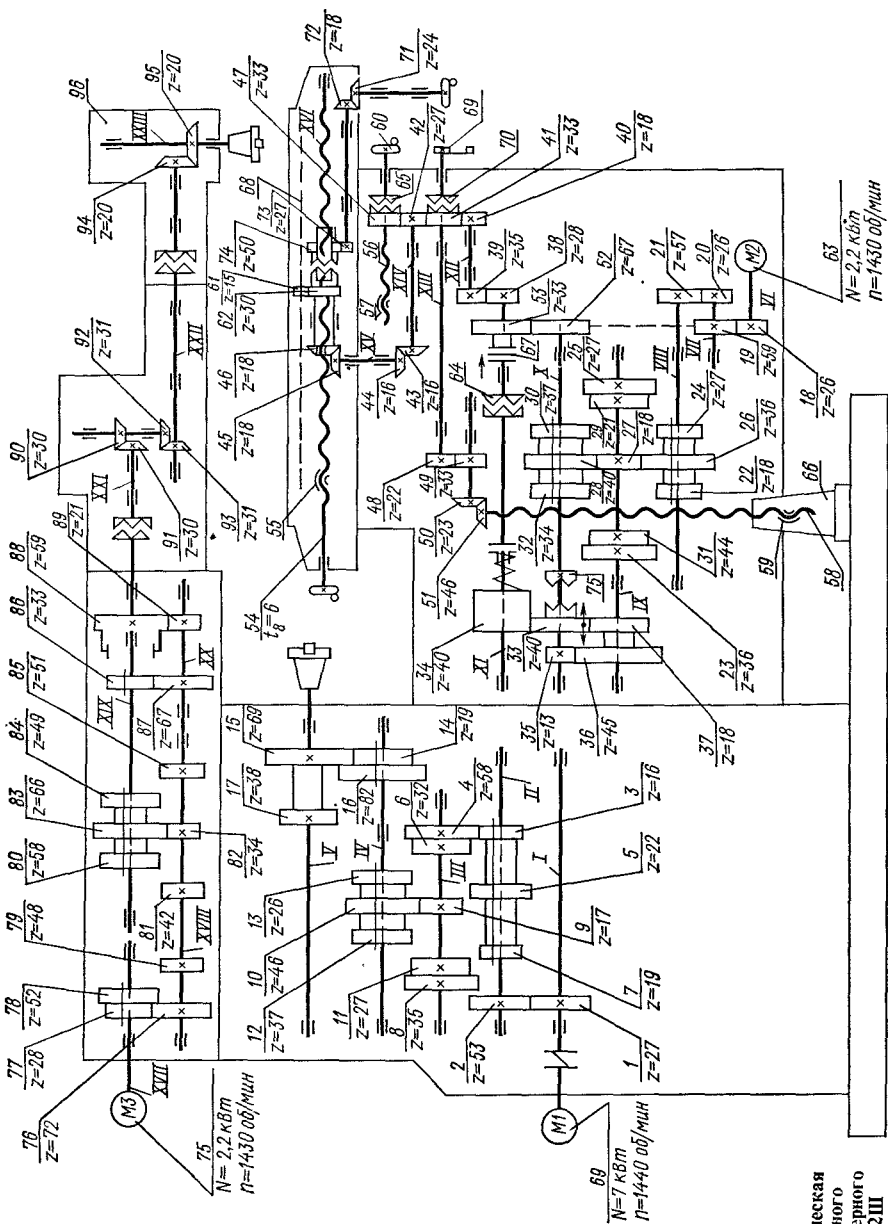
Кинематическая схема универсального горизонтально-фрезерного станка мод. 6Р82Ш
